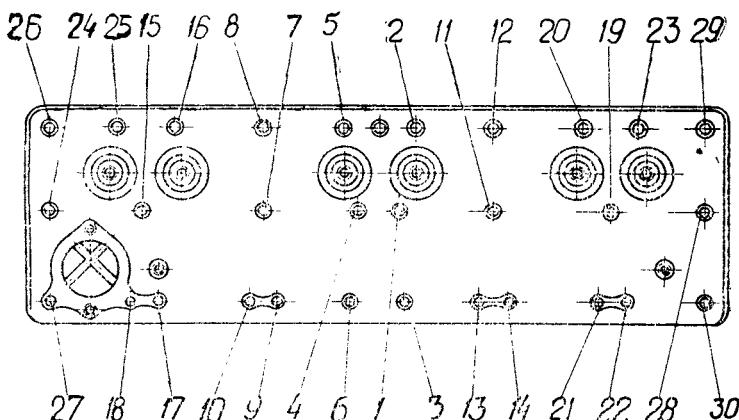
Порядок затягивания болтов и гаек крепления головки блока цилиндров.
